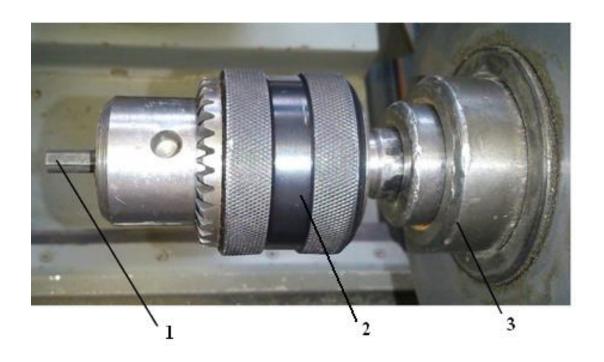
Закрепление заготовки - 1 - заготовка; 2 – патрон, 3 - оснастка;
